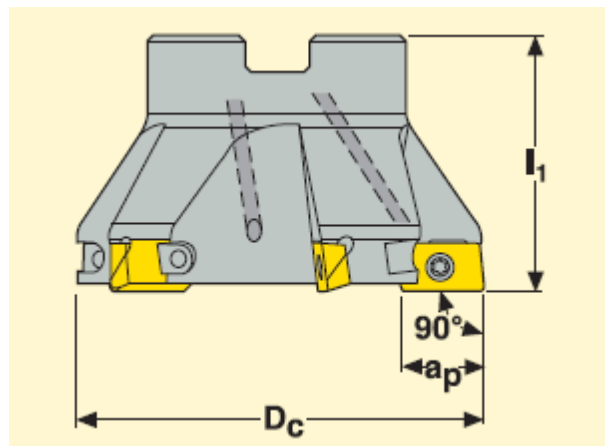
Фреза для врезного фрезерования R217.69–0814.RE-15-06.2N
